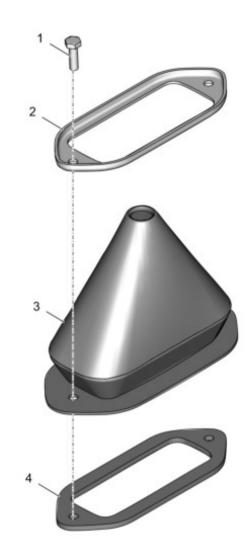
4320-1804004 Установка уплотнителя рычага на кожухе пола
